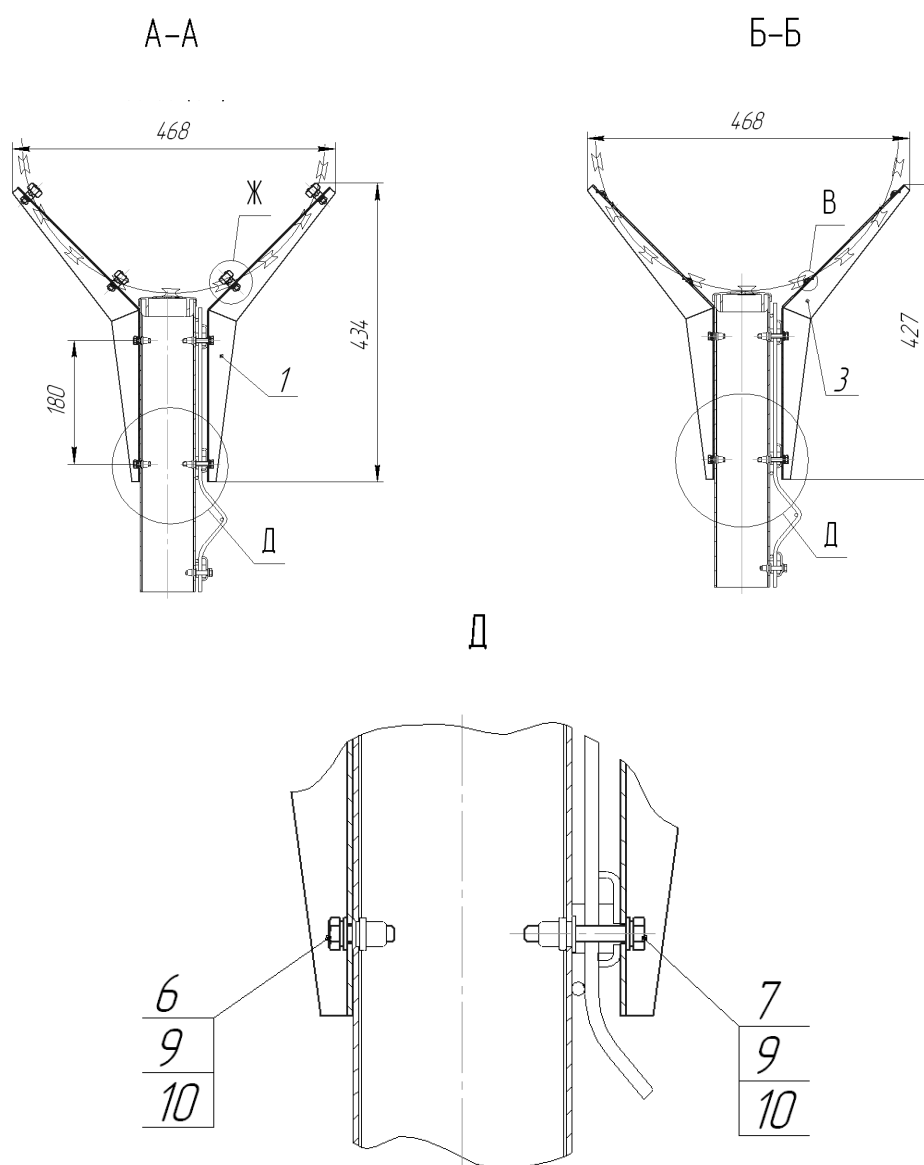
Разрезы А–А, Б–Б, детальный вид Д
